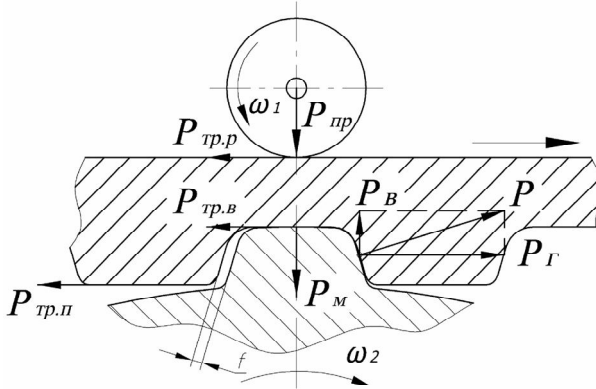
Розрахункова схема зачеплення зубчато-шліцьового вала з конвеєрною стрічкою в установці для її розрізання на смуги
